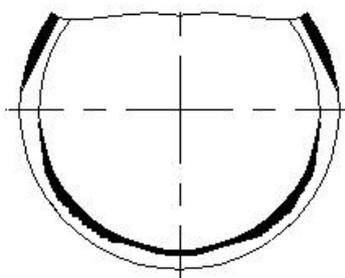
Зона блестящего пояска при резке ножом с выемкой
